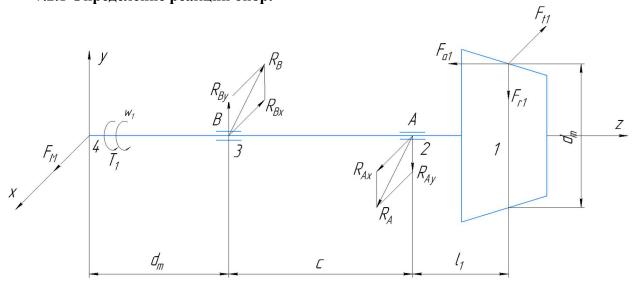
Схема нагружения подшипников быстроходного вала.
